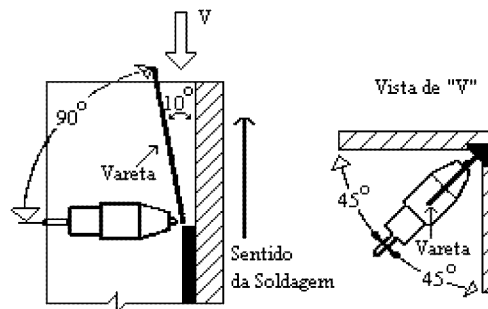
Soldagem TIG de Filete na Posição Vertical-Ascendente.
